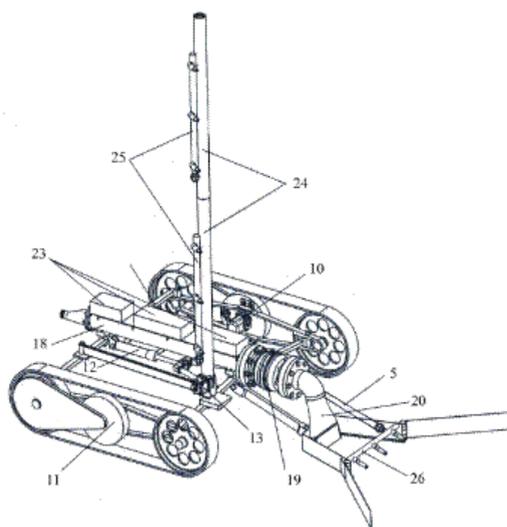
б — Тележка с разведенными колесными парами и установленными на ней всасывающей трубой и распылительными приспособлениями
